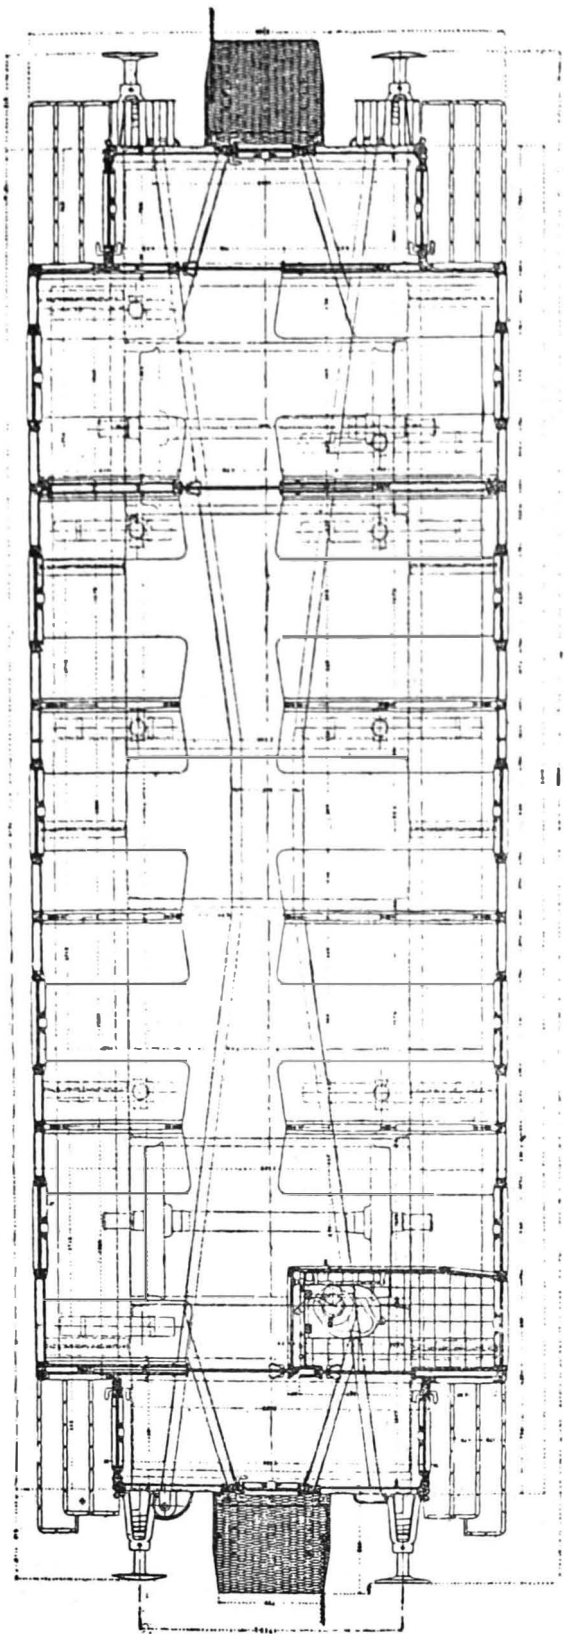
Planul vagonului de călători, cl. III, construit în 1898.
